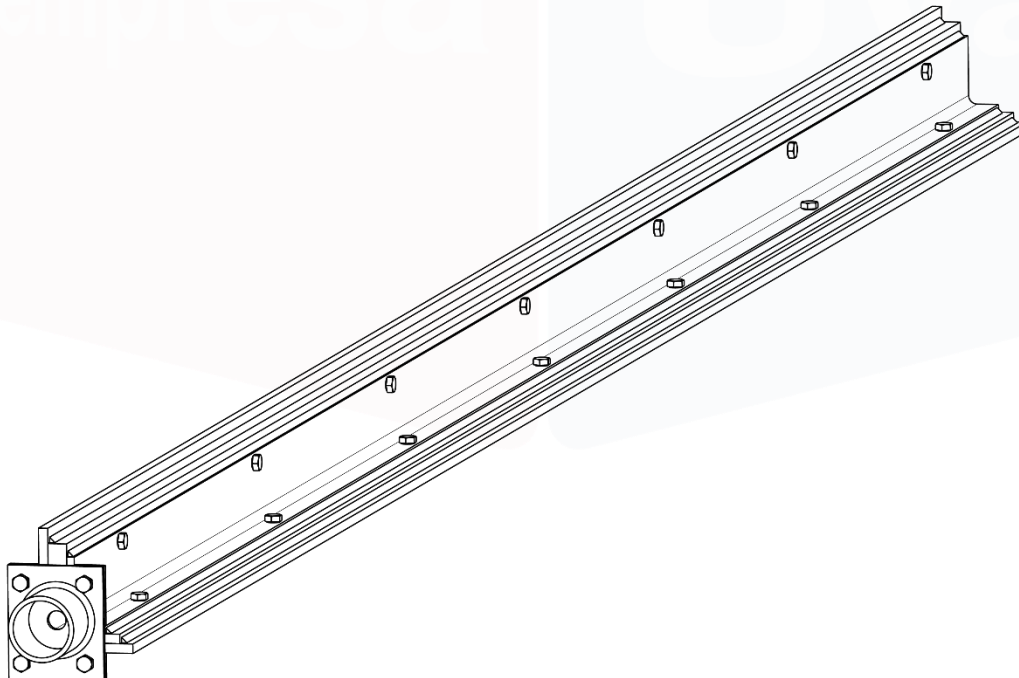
Vista extraída de los planos de fabricación del molde de extrusión
